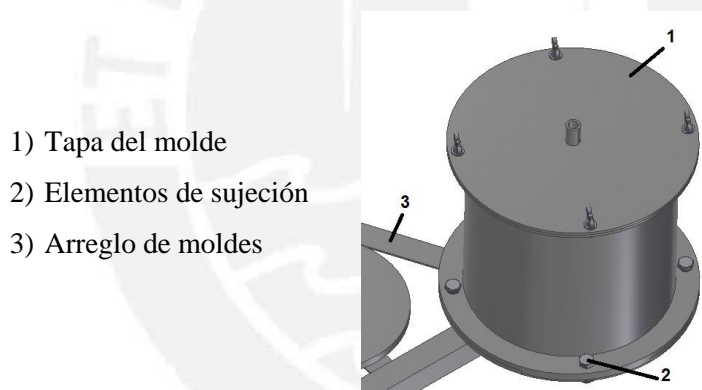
Acople del molde cilíndrico al arreglo de moldes.
